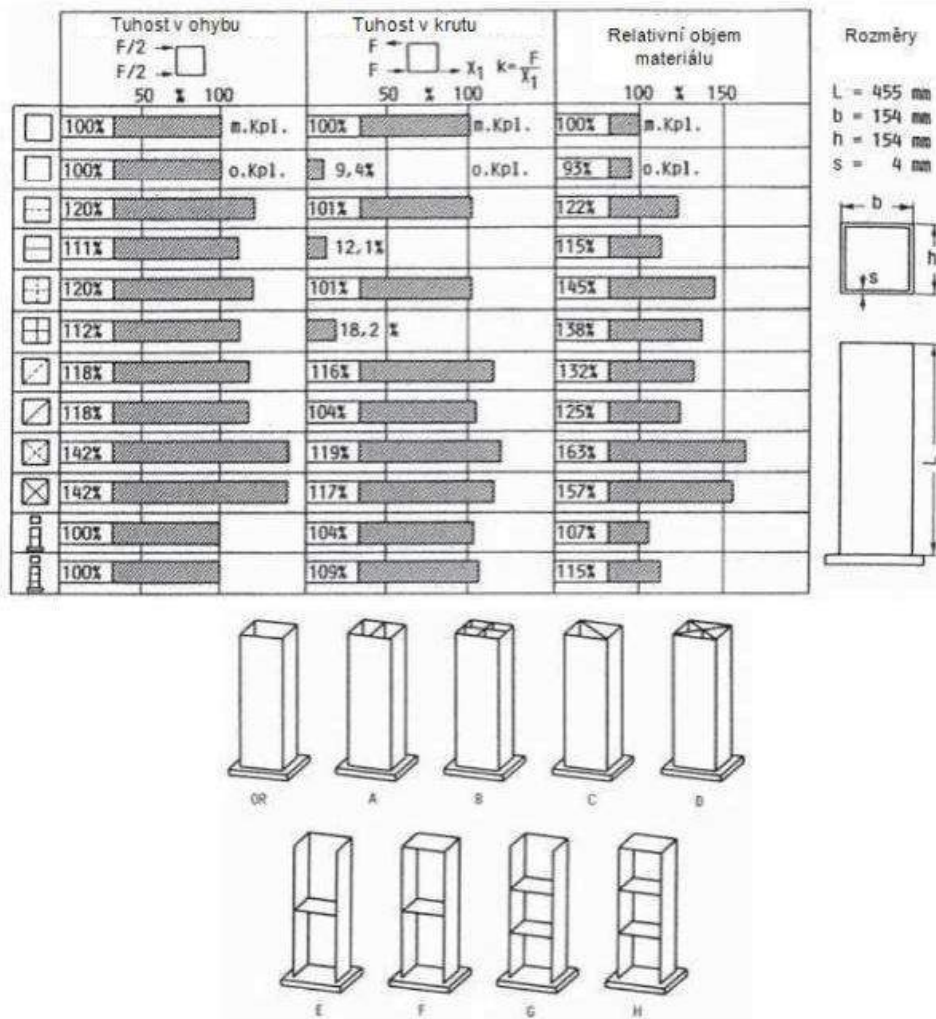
Prvky nosné soustavy obráběcích strojů [5]
